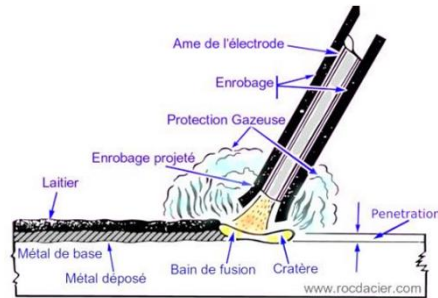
Schéma d'assemblage par soudage .
